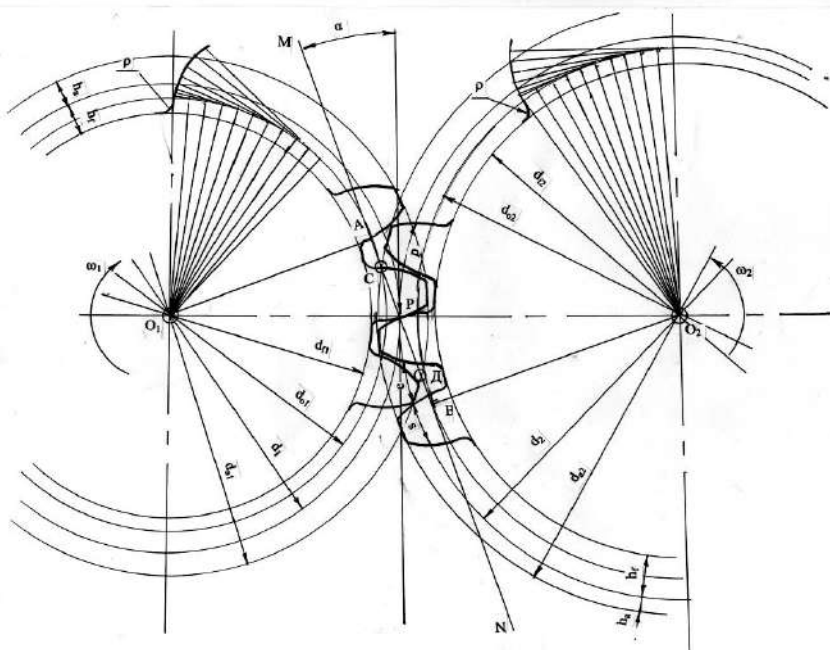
Эвольвентное зацепление зубчатых колес
